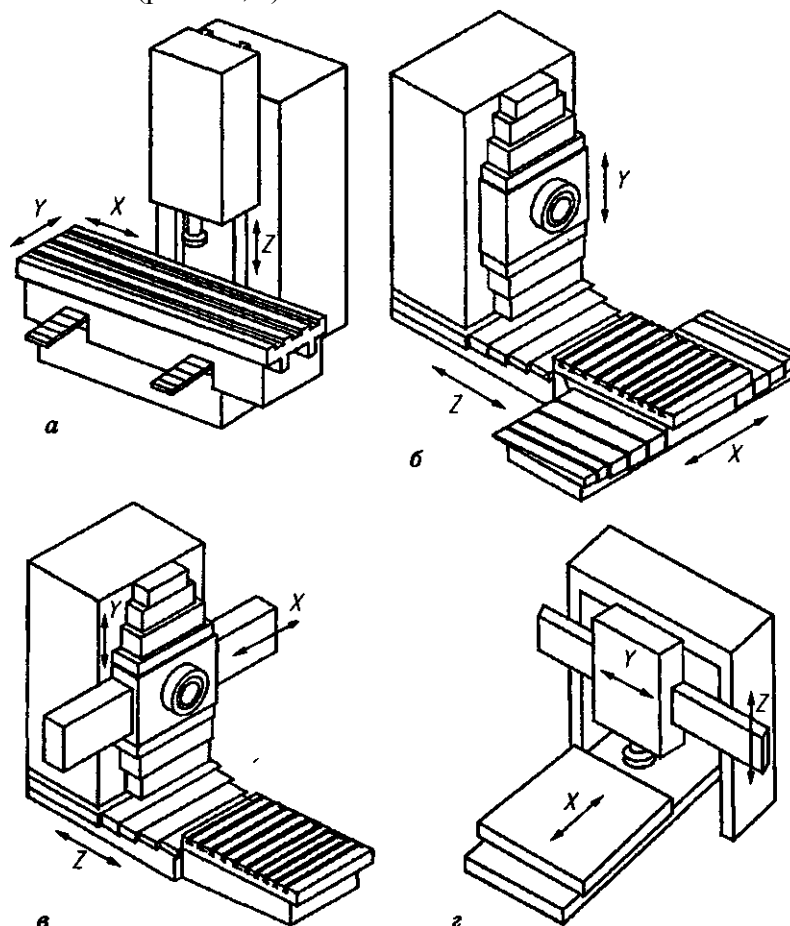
Компоновочные схемы станков сверлильно-фрезерно-расточной группы
